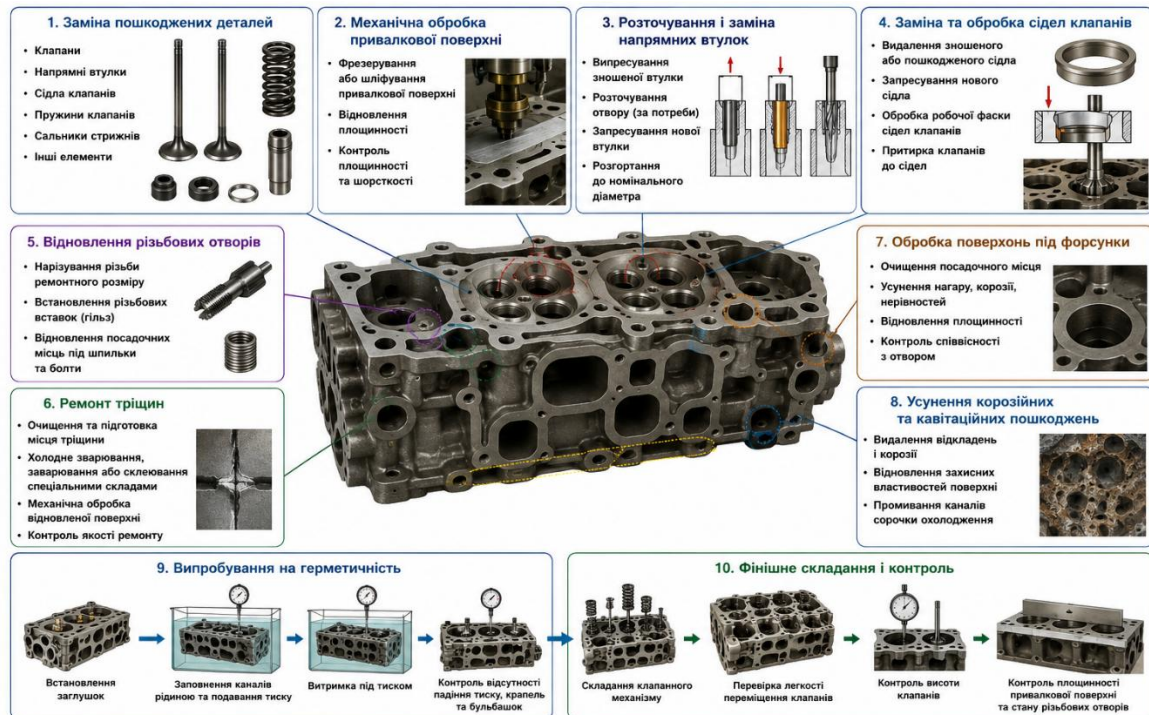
Основні напрями ремонту головки блока циліндрів.
